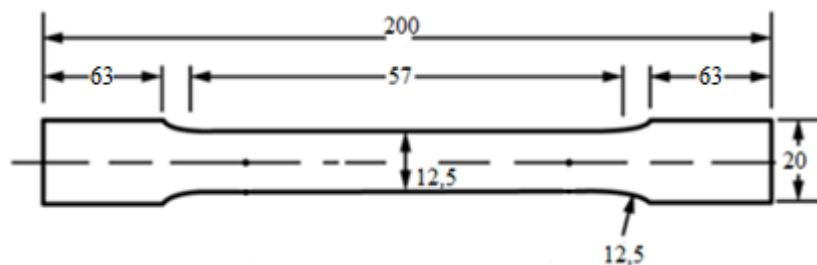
Dimensões do corpo de prova utilizado para os ensaios de fadiga. Fonte: Autor.
